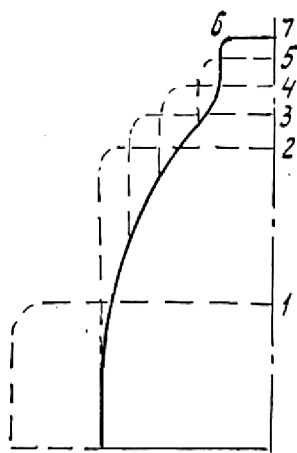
Последовательность штамповочных переходов при изготовлении кожуха камеры сгорания: 1-6 - вытяжка, 7-калибровка
